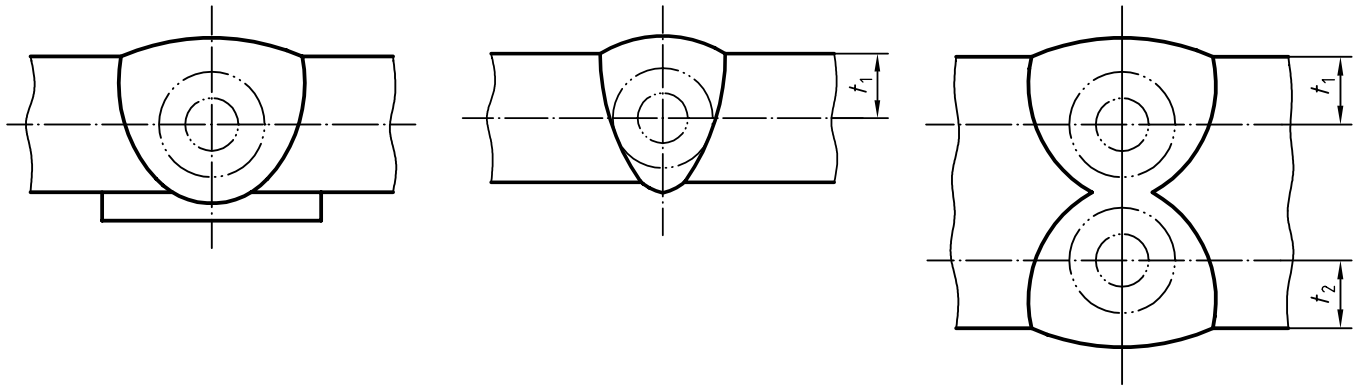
Exemple d'emplacement des éprouvettes — Coupe longitudinale
